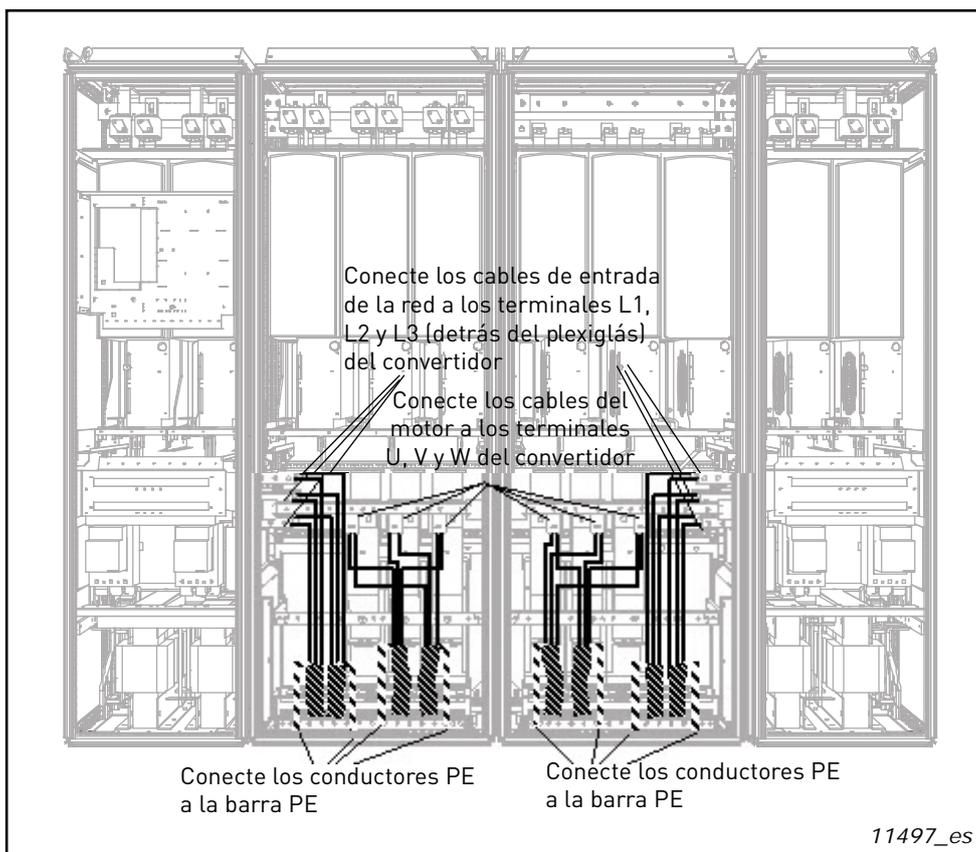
Colocación de los cables de alimentación, cableado inferior, bastidor FR14
